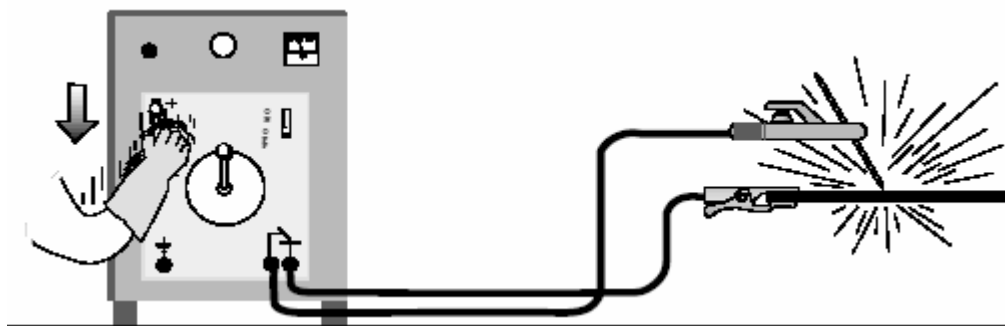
Equipo para soldadura de arco eléctrico
